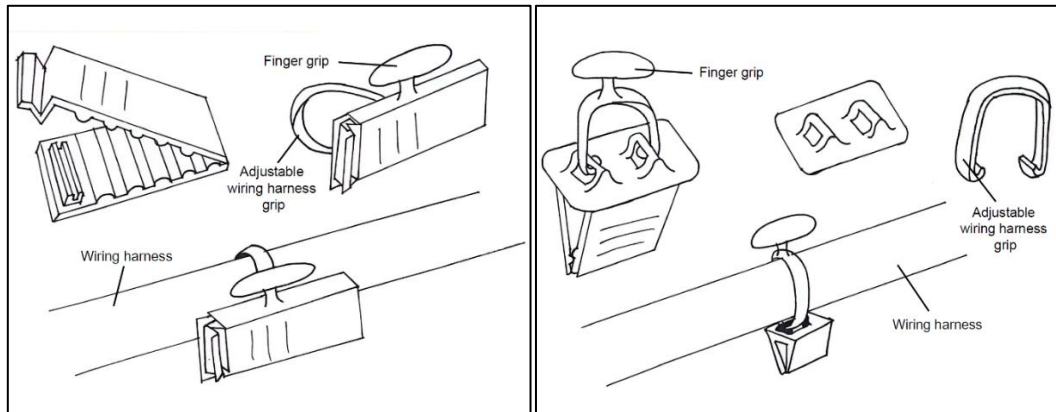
Concepto 5 y 6 del Clip Plano. Fuente: Elaboración Propia.
